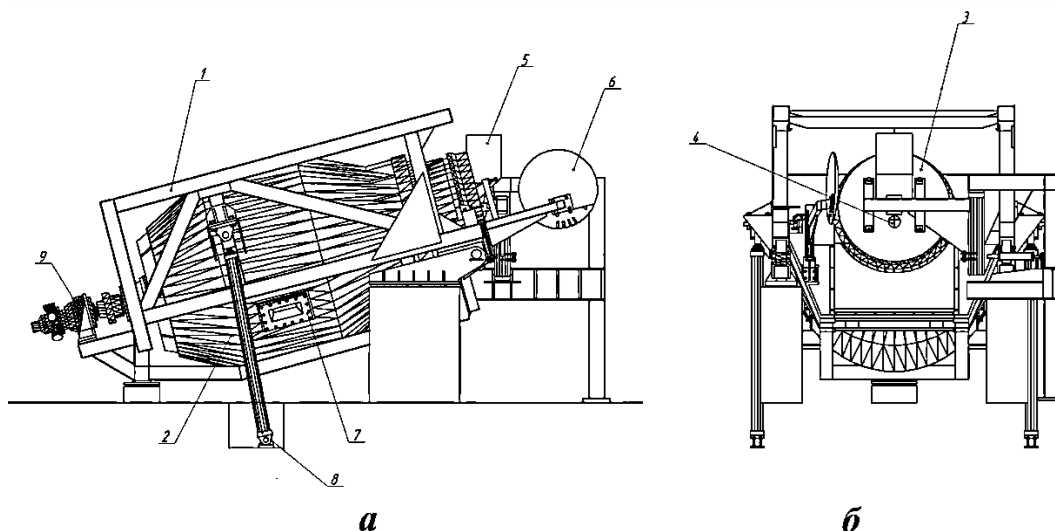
Основные детали роторной наклонной печи РНП-10: а – вид сбоку, б – вид с торца, 1 - поворотная рама, 2 - корпус печи, 3 – горелочный щит (крышка печи), 4 - газовая инжекторная горелка, 5 - патрубок для вывода отходящих газов из печного пространства, 6 – жароотражатель, 7 – окно для измерения температуры печи, 8 - гидроцилиндр подъёма, 9 – электропривод вращения печи.
